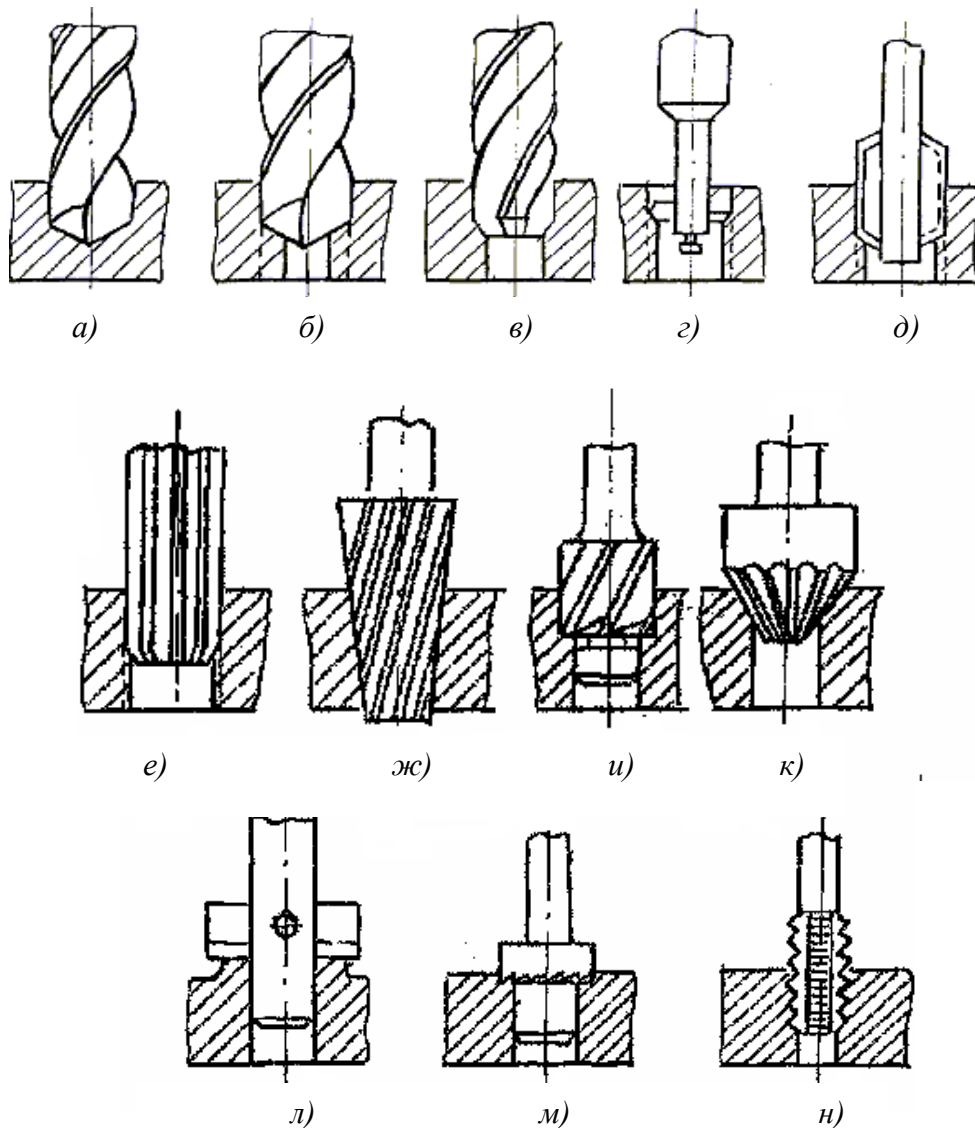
Схеми одержання і обробки отворів на свердлильних верстатах
